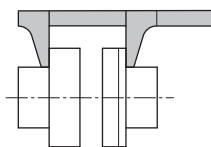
Kontrola radiálnej adjustácie pomocou pravítka
